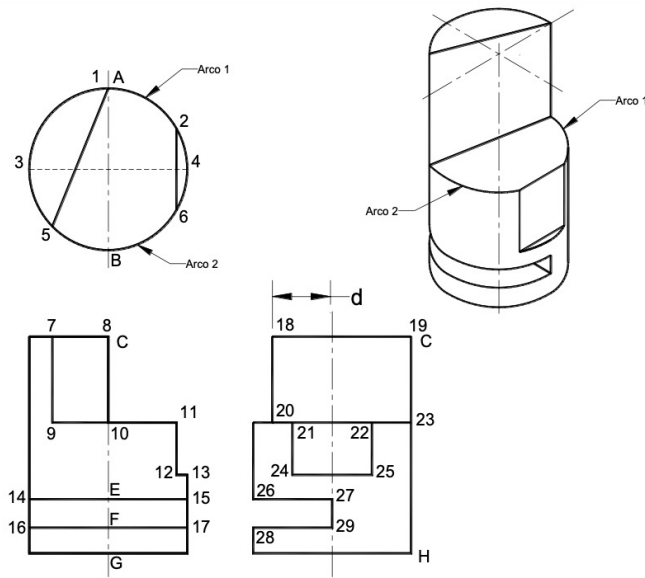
Ejemplo de aplicación sobre Vistas Auxiliares. Fuente [15]
